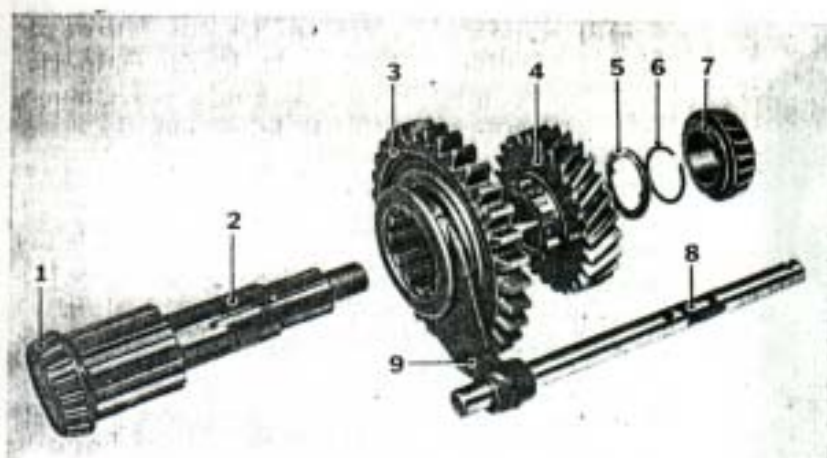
Despiece del eje de salida delantero con sus engranajes.
